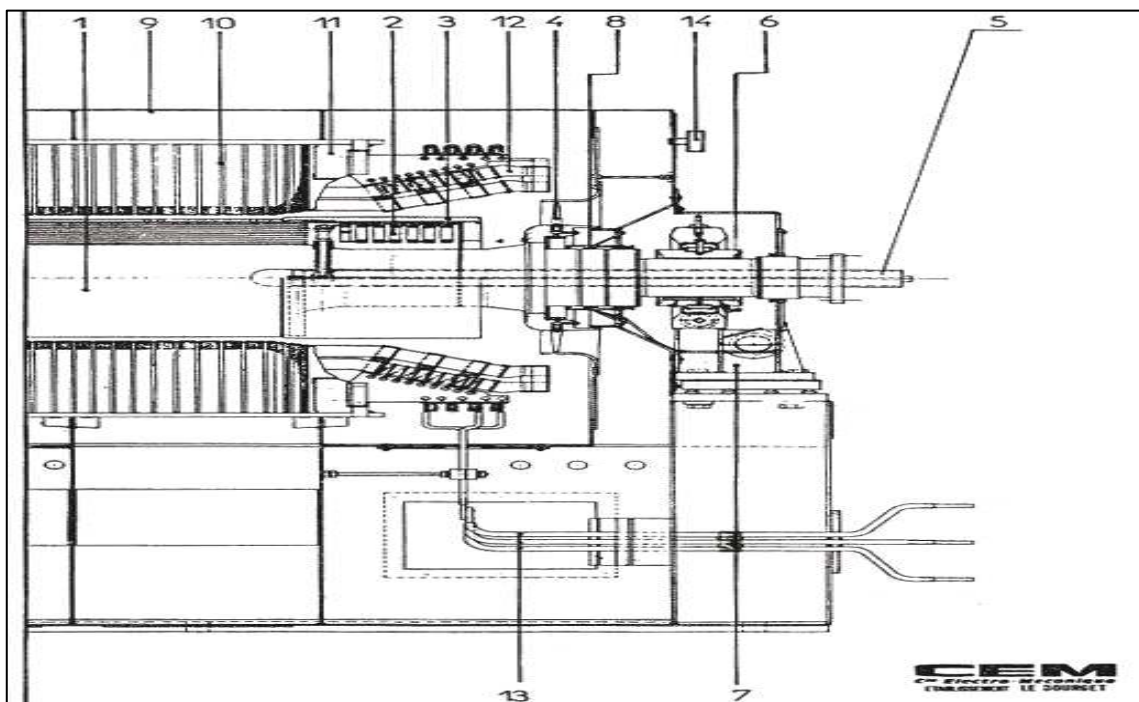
Schéma en coupe d'un alternateur de la centrale
